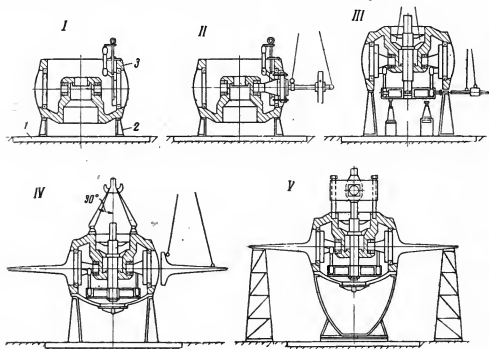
Схема сборки рабочего колеса крестовинного типа с кантовкой втулки.
